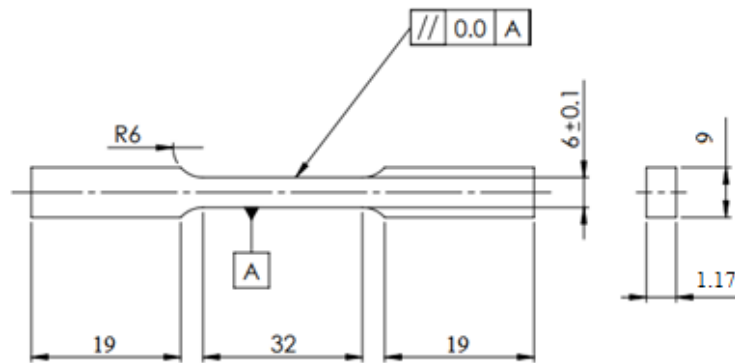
Dimensiones de la probeta para ensayo según la norma ASTM E 8
